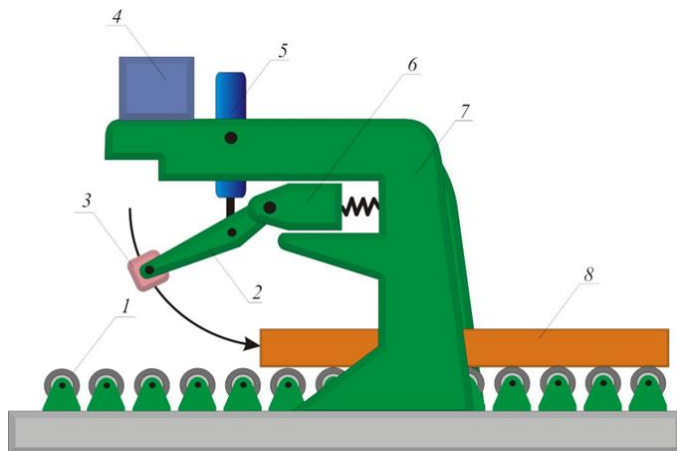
Клеймитель: 1 – рольганг; 2 – рычаг; 3 – молоток; 4 – кассета с клеймами; 5 – гидроцилиндр; 6 – подпружиненный упор; 7 – станина; 8 – блюм (сляб)
